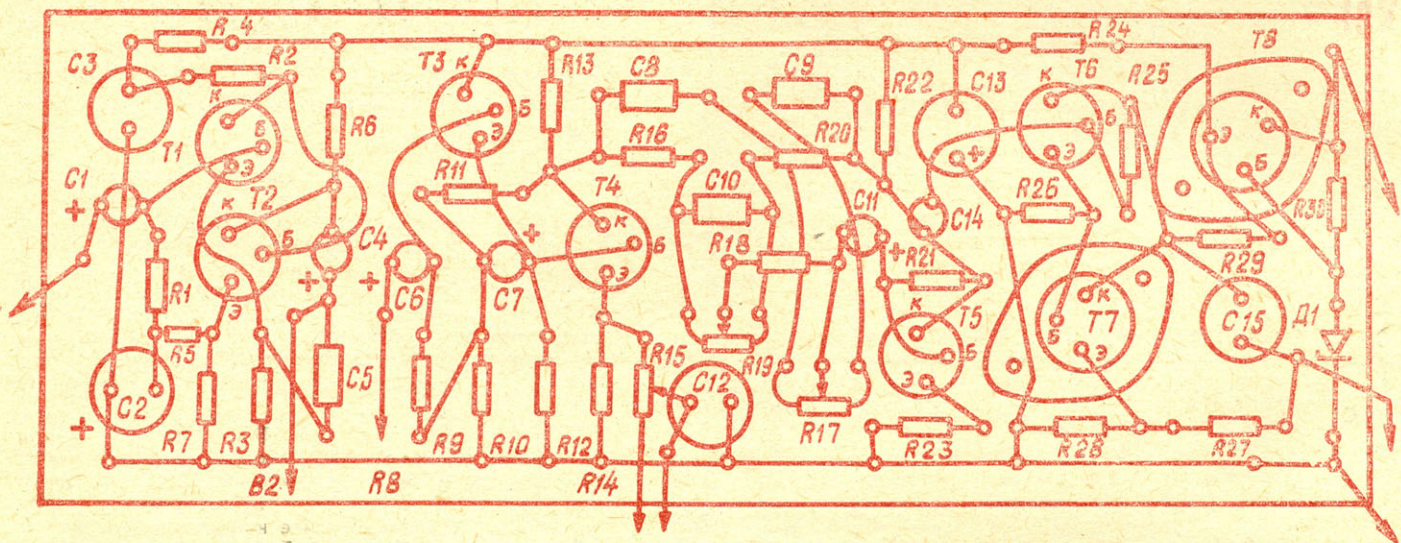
Печатная плата одного канала усилителя с расположением деталей.
